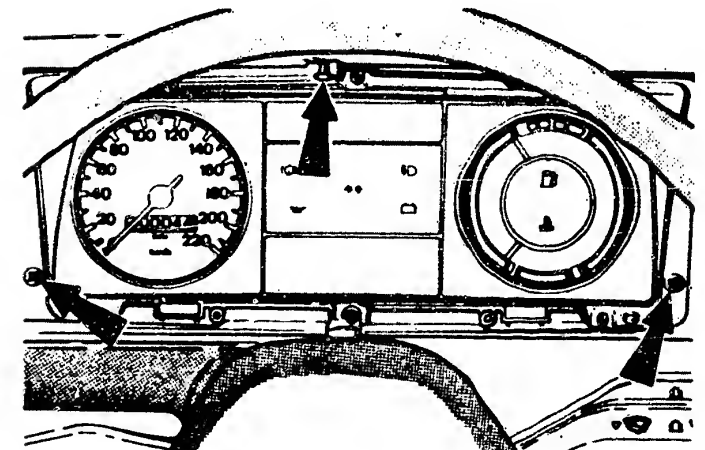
Die Pfeile zeigen die Befestigungsschrauben des Kombi-Instrumentes an.
